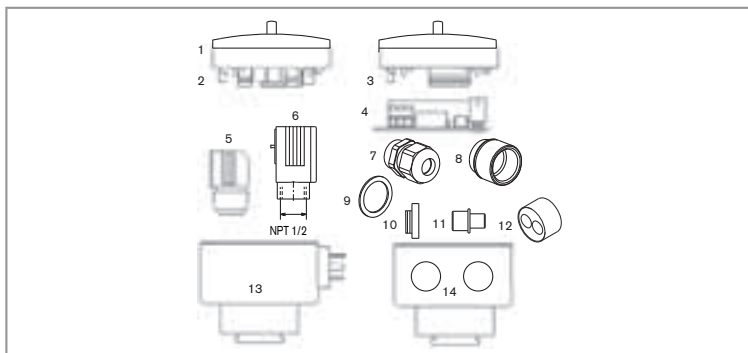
Vue éclatée des pièces de rechange du 8035
